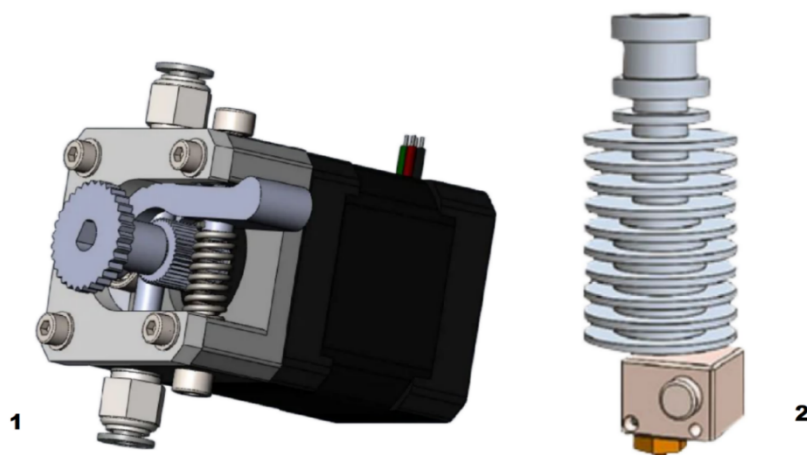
Комплект для 3D печати. 1 – экструдер для подачи пластика, 2 – печатающая головка
